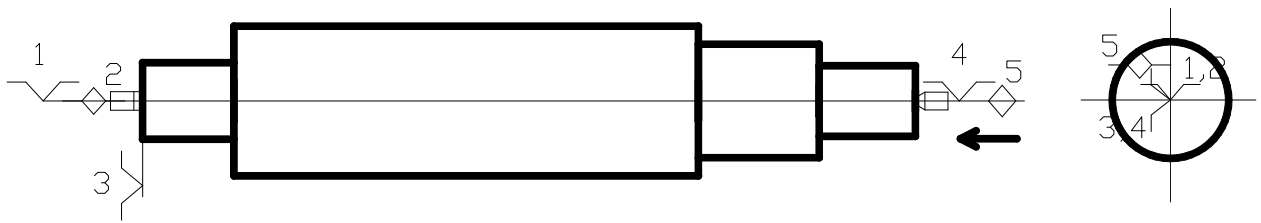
Чистові технологічні бази при обробленні поверхонь обертання в центрах
